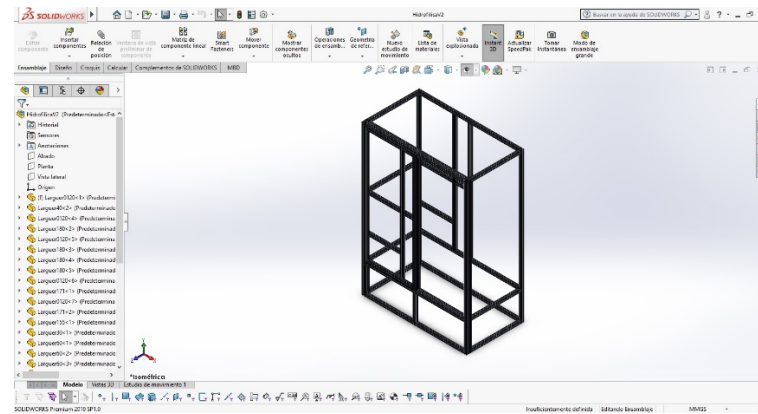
Herramienta SolidWorks para diseños 3D utilizado en manufactura
